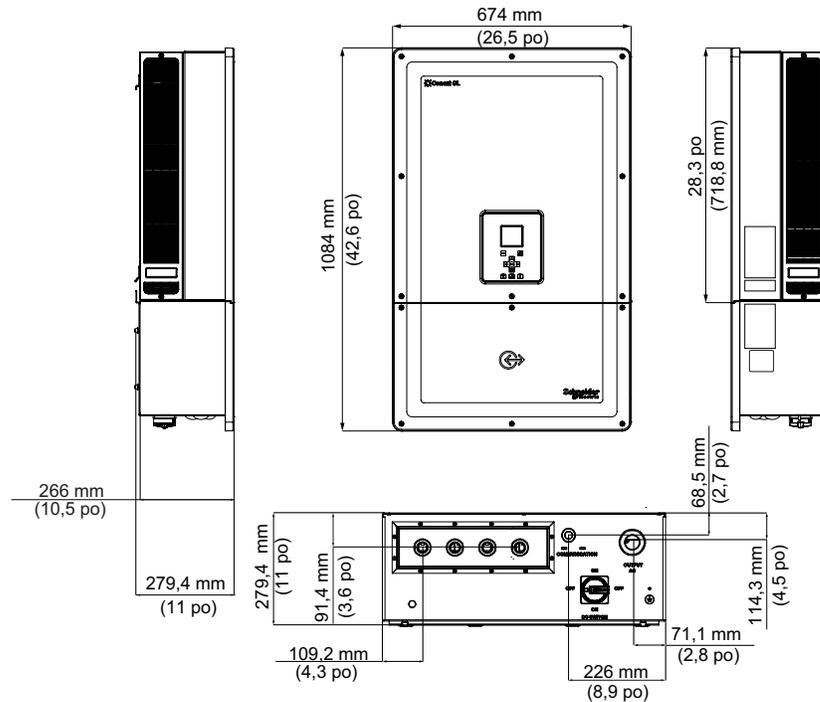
Vues et dimensions de l'onduleur et du boîtier de câblage (Essential/Optimum)
